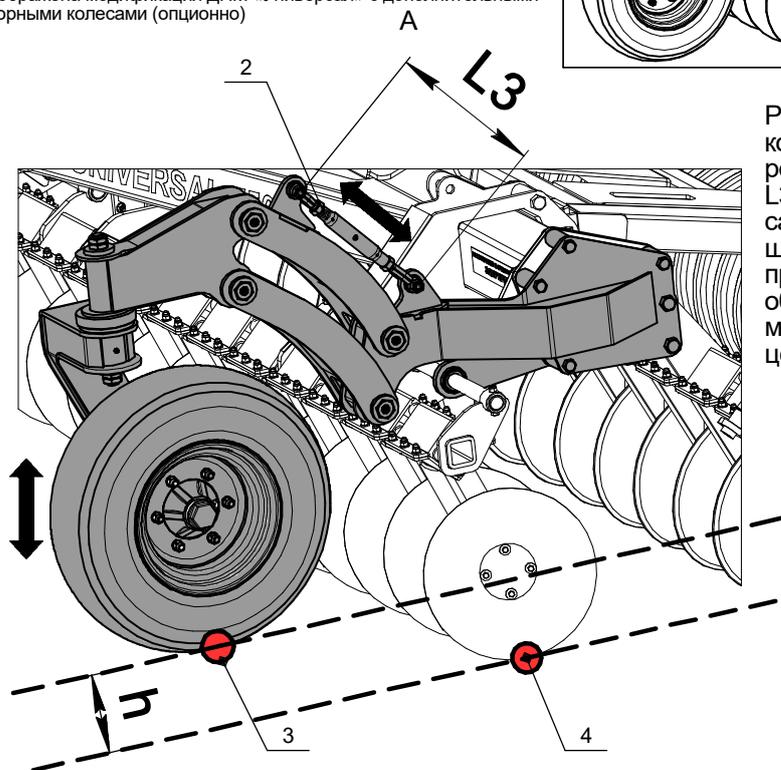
Регулировка рабочей глубины дисковой почвообрабатывающей машины ДПМ-5000, ДПМ-6000 "Универсал" / "Универсал Т"
